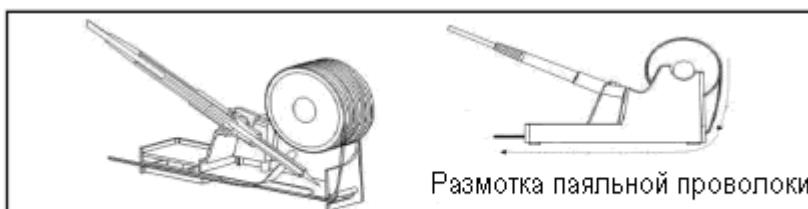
Подставка для паяльника с держателем для паяльной проволоки
